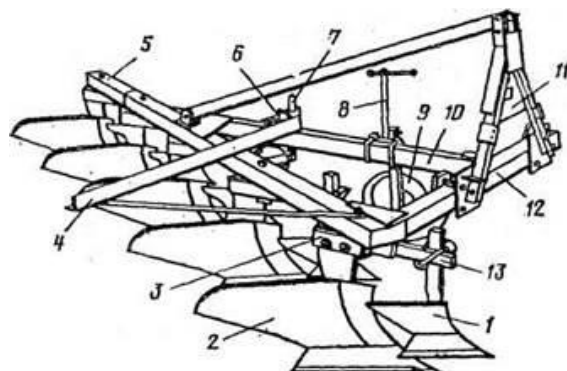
Плуг ПЛН-5-35: 1 – предплужник; 2 – корпус; 3 – угольник; 4 – прицепка для борон; 5 – главная балка; 6 – кронштейн крепления ножа; 7 – дисковый нож; 8 – винтовой механизм; 9 – опорное колесо; 10 – продольная балка; 11 – замок автосцепки; 12 – поперечная балка; 13 – кронштейн предплужника
